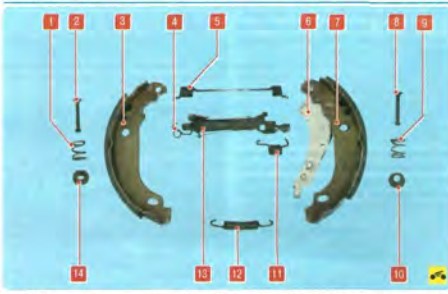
Детали тормозного механизма заднего колеса полноприводного автомобиля (показаны детали тормозного механизма с левой стороны): 1, 9 – прижимные пружины; 2, 8 – опорные стойки; 3 – передняя колодка тормозного механизма заднего колеса; 4 – серва регулятора зазоров; 5 – верхняя стальная пружина; 6 – разжимной рычаг привода стояночного тормоза; 7 – задняя колодка тормозного механизма заднего колеса; 10, 14 – чашки прижимных пружин; 11 – оттяжная пружина распорной планки; 12 – нижняя стальная пружина; 13 – распорная планка с регулятором зазоров
